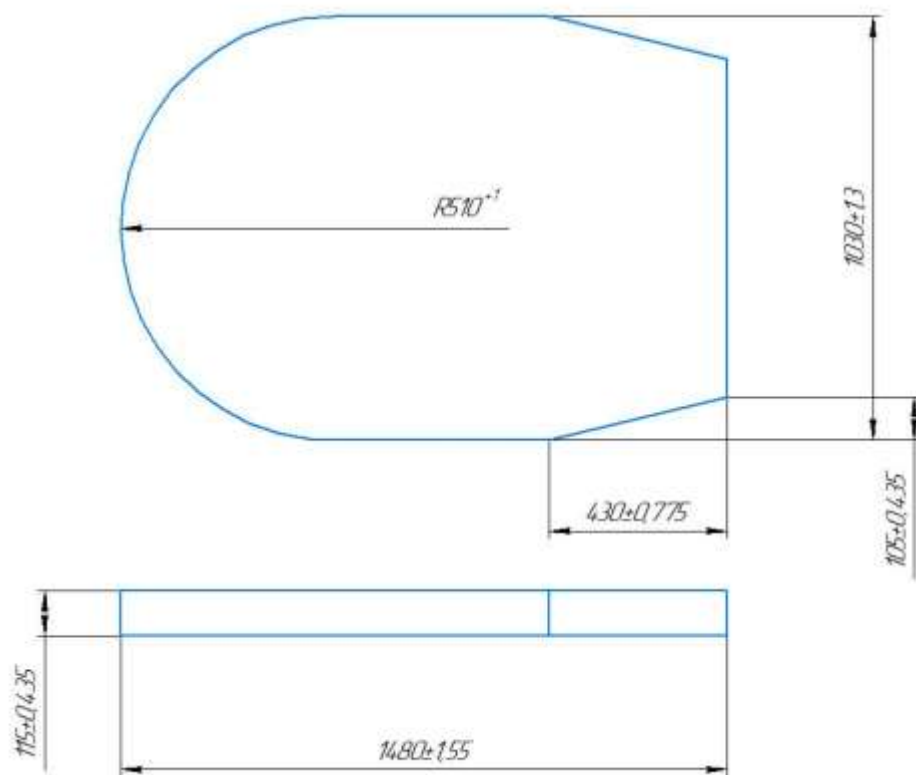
Ескіз заготовки деталі «Кришка»
